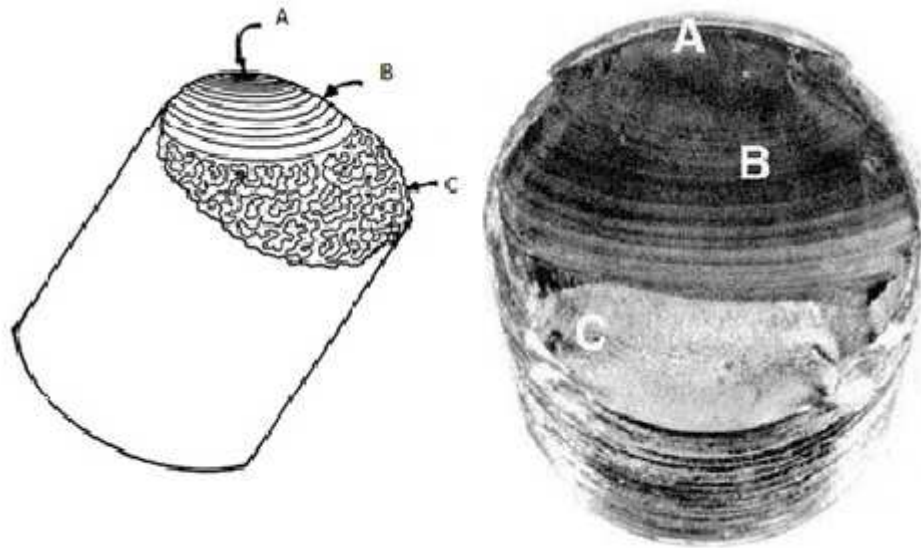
Falha fadiga em um eixo. Zona A - começo da falha; Zona B - Propagação da falha na maior parte da secção transversal (marcas de praia); Zona C - Falha final por fratura.
